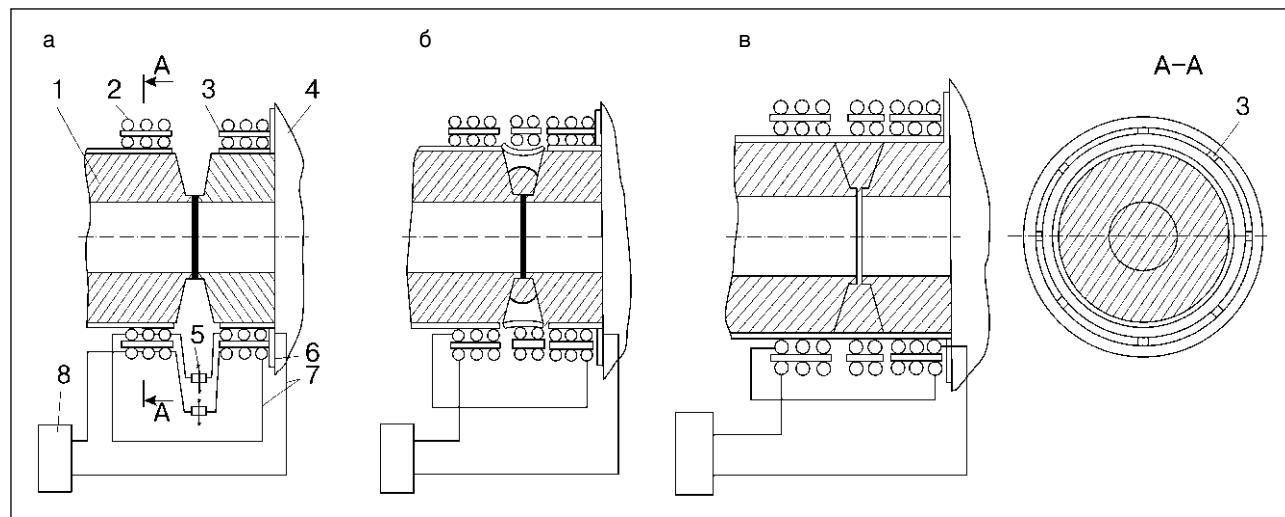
Схемы установки индукторов при термообработке стыков патрубков агрегатов Тольяттинского азотно-турового завода: а — при подогреве под сварку; б — при промежуточной термической обработке; в — при окончательной термической обработке (1 — труба; 2 — индуктор; 3 — асбоцементные планки; 4 — конвертор; 5 — болтовые соединения; 6 — теплоизоляция; 7 — токоподводящие провода; 8 — трансформатор ТДФ-1601)
